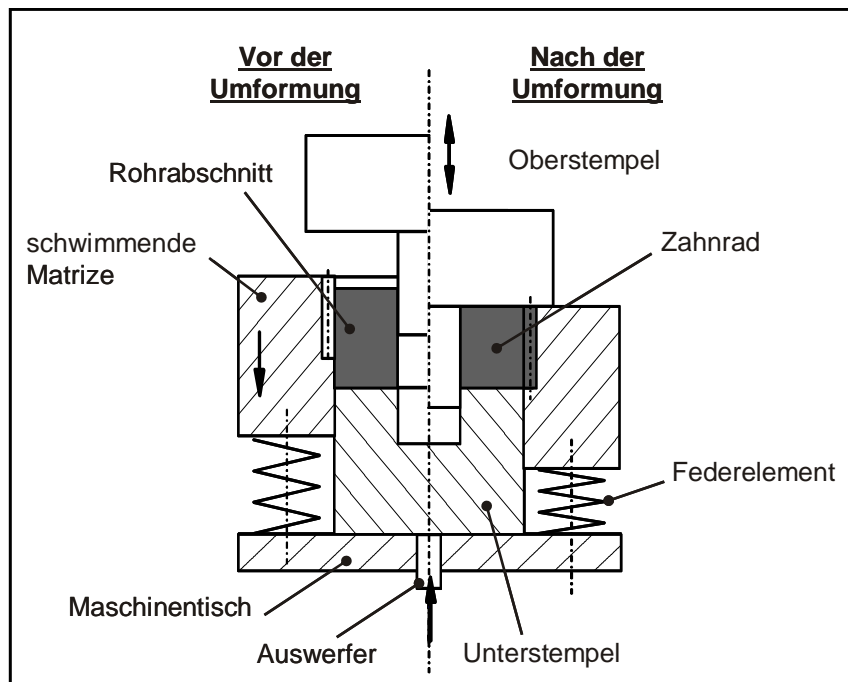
Werkzeugsystem mit schwimmender Matrize zum Präzisionsschmieden von Zahnrädern nach [BDR04]
